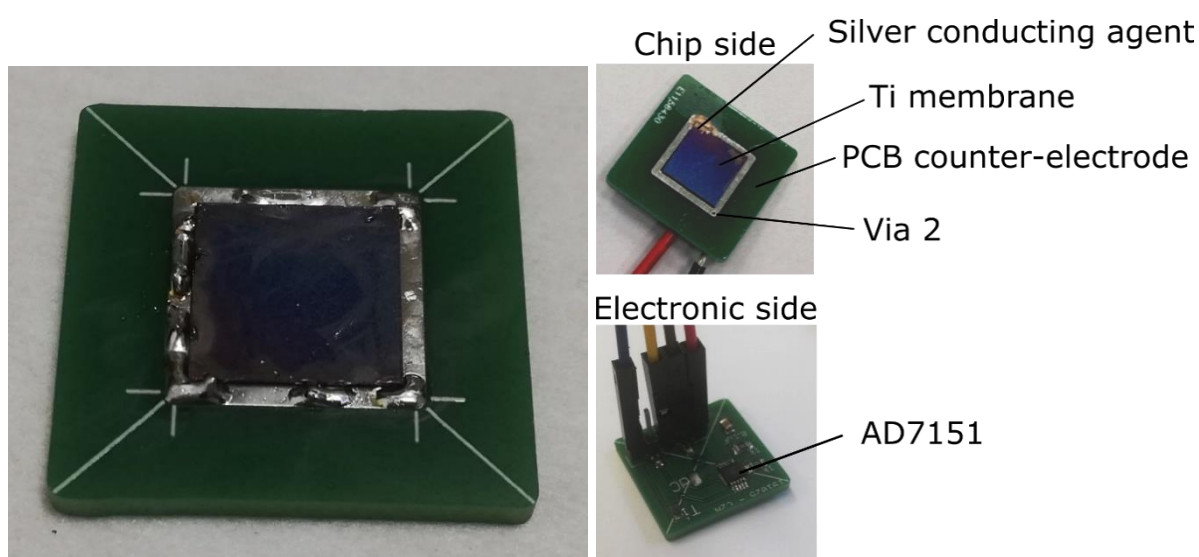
à gauche, membrane titane soudée à un PCB. A droite, une puce assemblée à un PCB grâce à film de résine.
